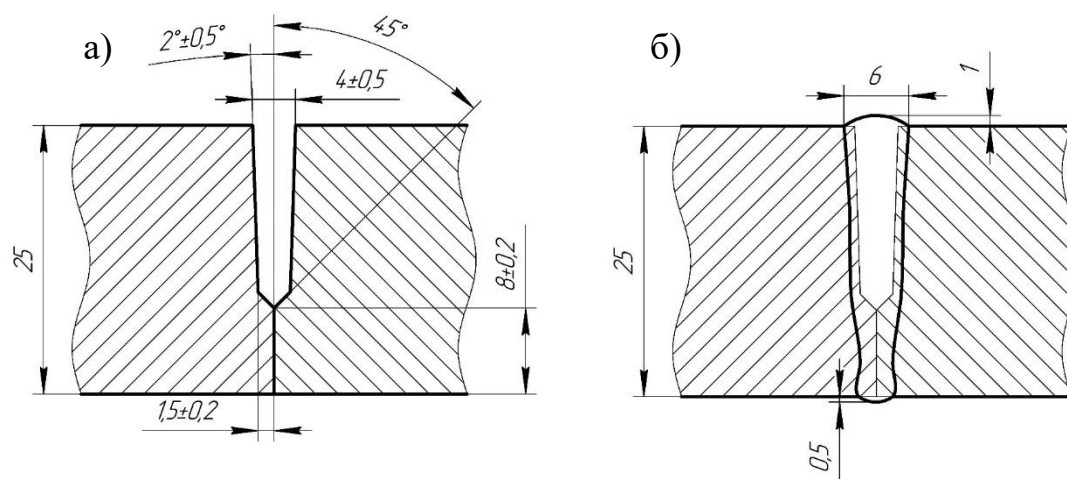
Лазерная сварка волоконным лазером: а) разделка кромок; б) поперечное сечение сварного шва.
